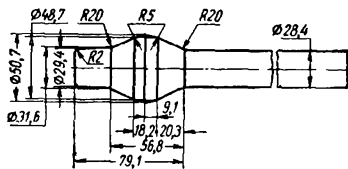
Высаженная на горизонтально-ковочной машине заготовка вала сошки
